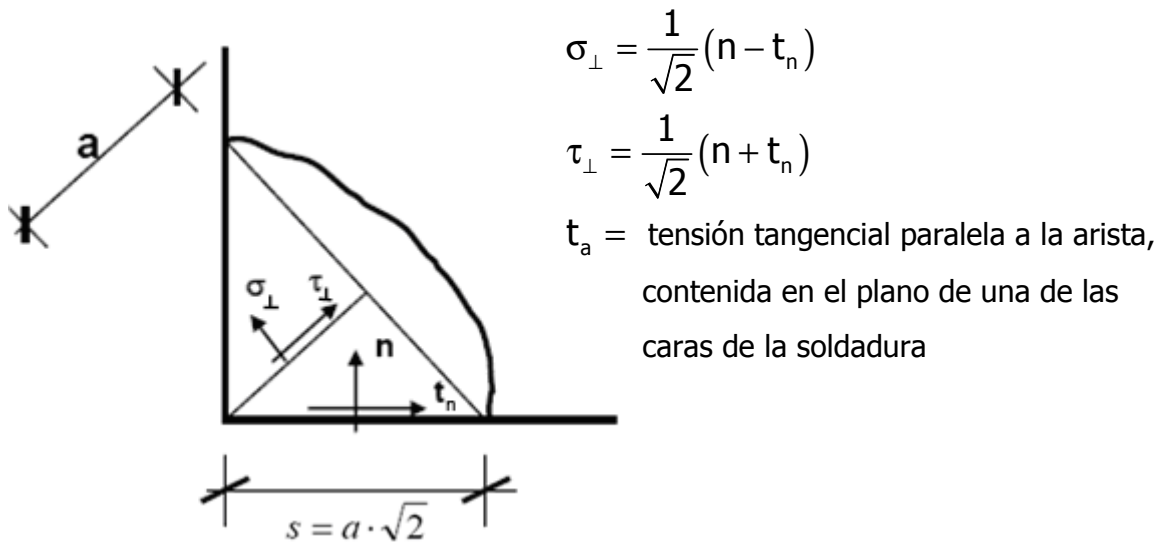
Tensiones en un cordón de soldadura.
